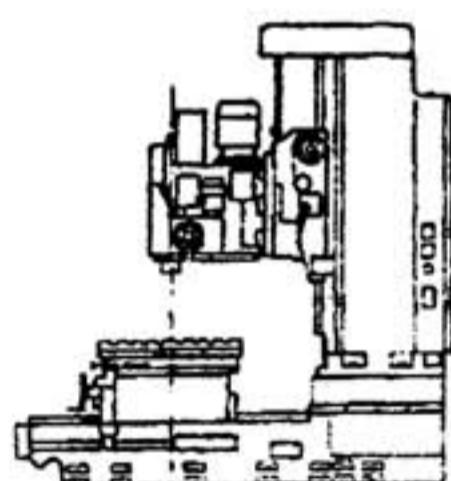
Универсальный фрезерный станок с поворотной фрезерной головкой
